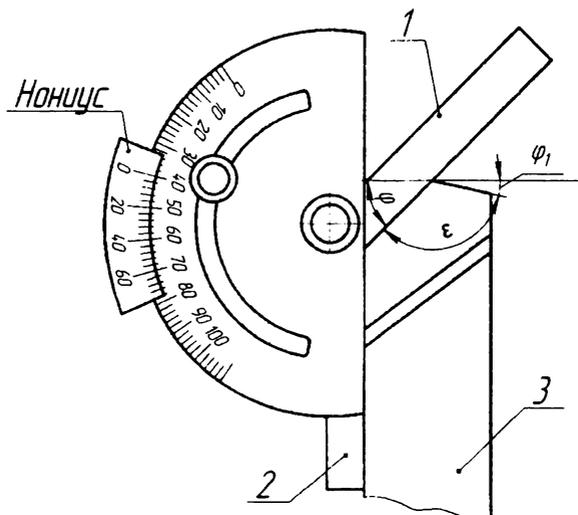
Схема измерения угла φ токарного проходного резца
